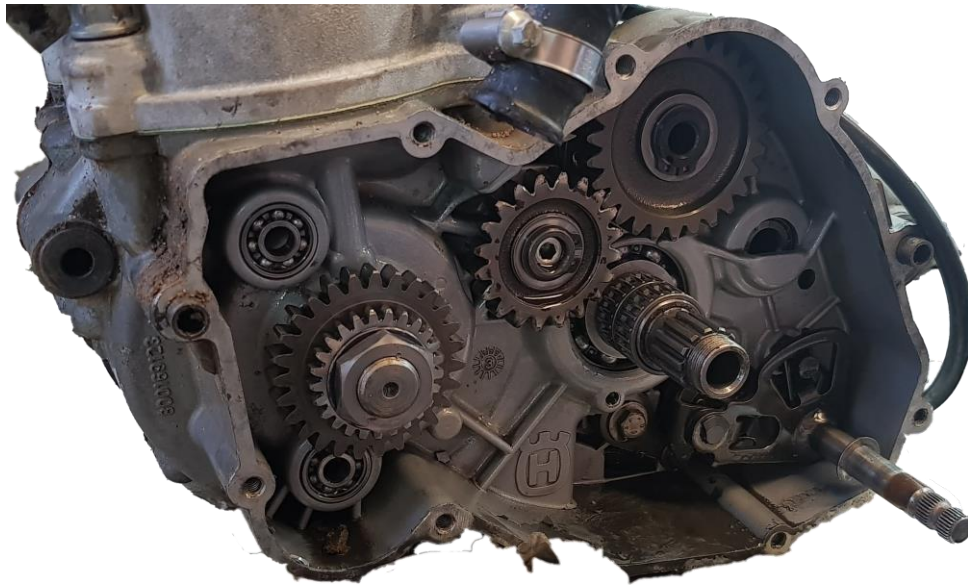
Vista del cárter izquierdo sin el conjunto del embrague.
